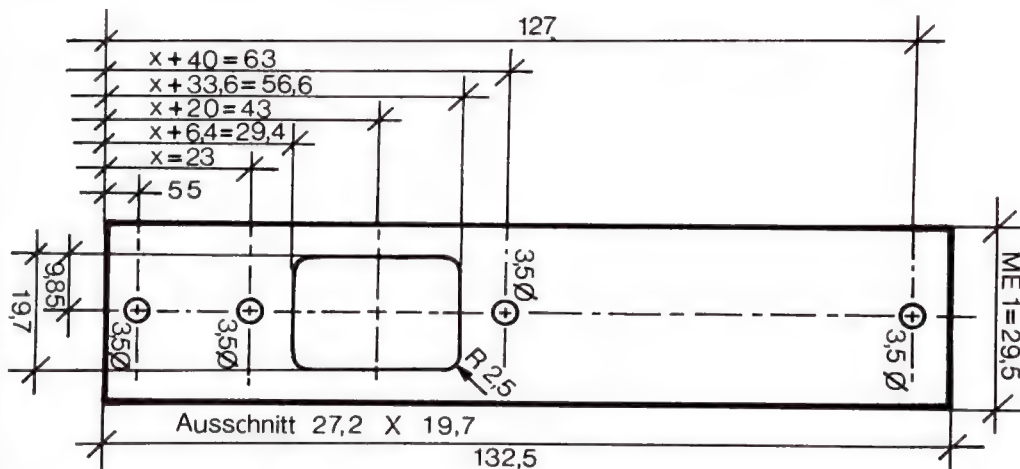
Maßskizze für die Steckerplatte. Auf dieser Zeichnung sind auch die zwei Bohrungen für die Befestigung der Platte auf den Gleitmutter-Kanälen des Gehäuses vermaßt.
